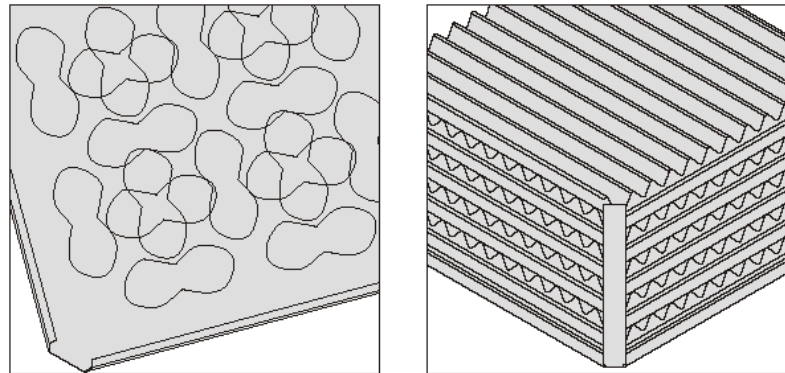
Formas de construcción de la distancia de laminas, estampado y perfiles ondulados
